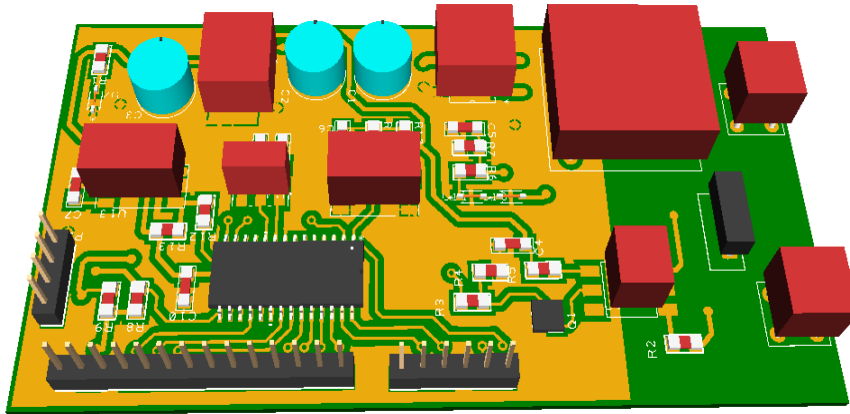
Vista 3D de la PCB diseñada para el proyecto.
